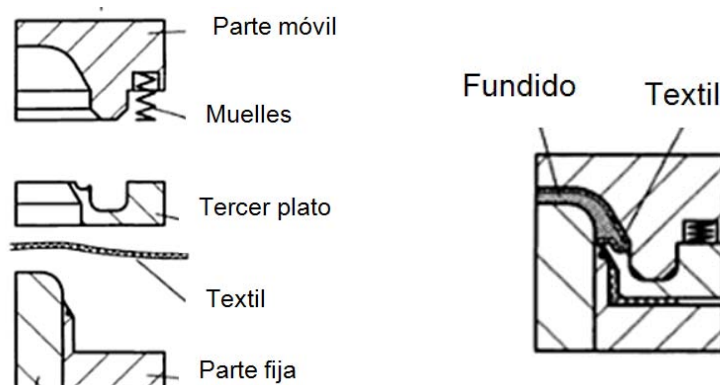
Diseño de molde para inyección sobre textil [29]
